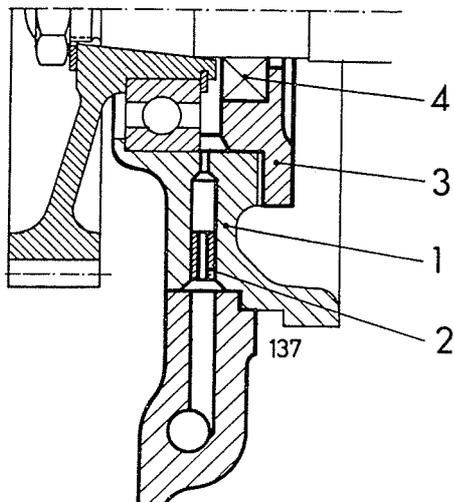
Einspritzpumpenantrieb F/A 4-6L 514 mit Bohrung für Schmierölaufuhr
